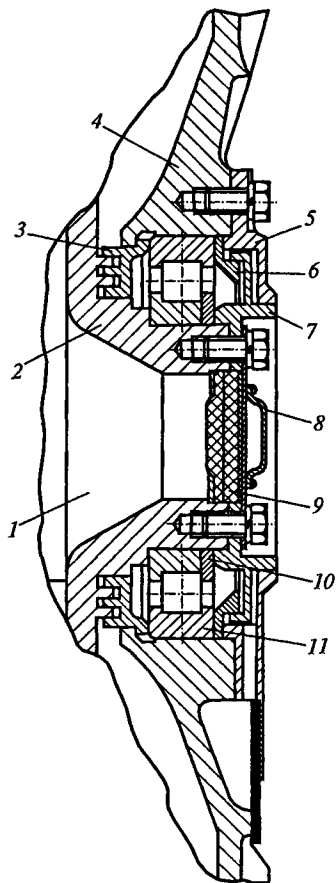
Большой подшипниковый щит электродвигателя НБ-520В:
